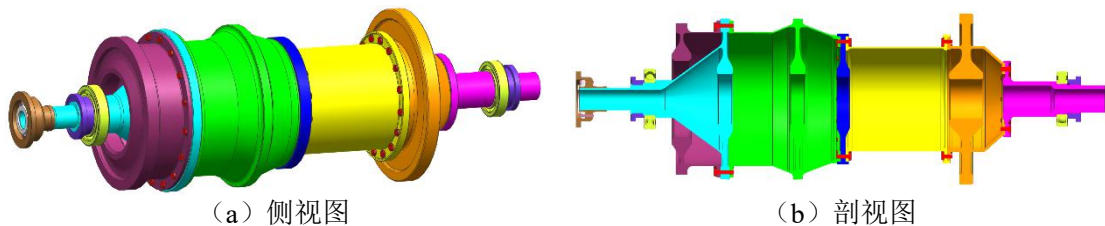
多连接面的高压转子模拟试验器 CAD 图
